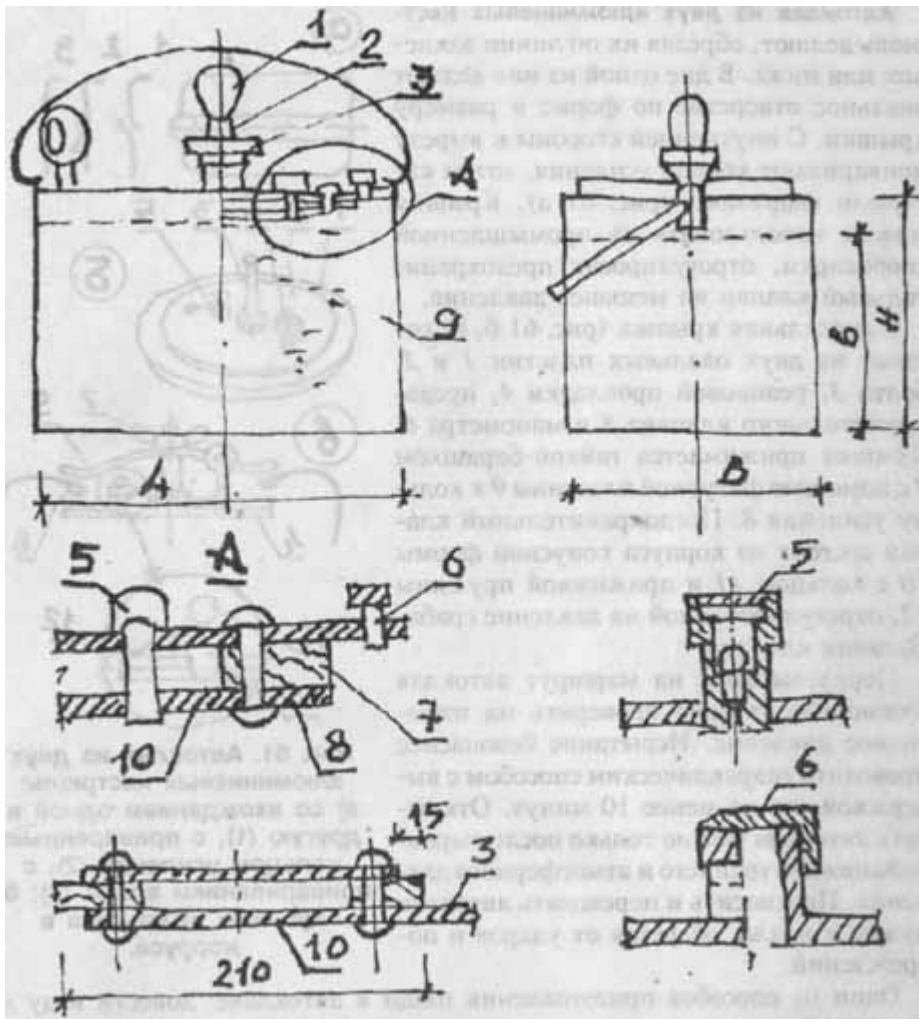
Автоклав со сварным корпусом и внутренней крышкой. 1. Теплоизоляционная ручки. 2. Винт М10. 3. Гайка-барашек. 4. Швеллер-замок. 5. Предохранительный клапан. 6. Штуцер сброса давления. 7. Резиновая прокладка. 8. Фланец крышки. 9. корпус. 10. Крышка. II. Манометр. I, И, II — длина, ширина и высота корпуса автоклава, h —уровень заполнения (I." 270—320 мм. U= 150—200 мм, H- 130—170мм, h - 100—150 мм; объем V- 10,0 л, полезный объем U_n 4,0—8,3 л).
